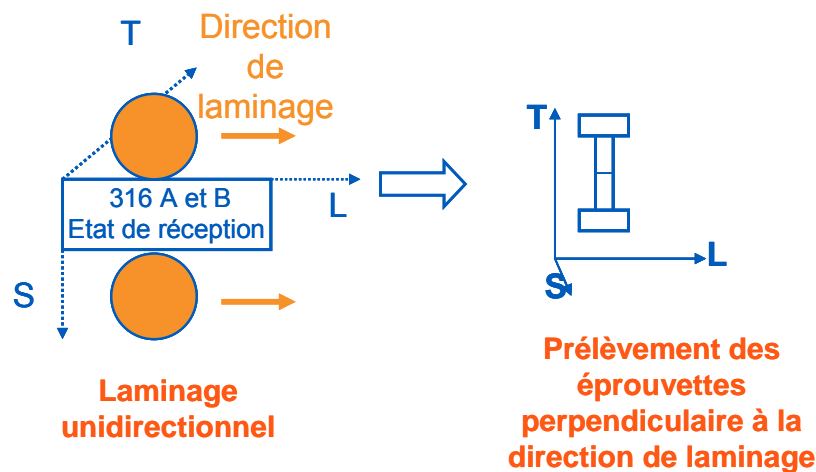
Laminage et prélèvement des éprouvettes en acier 316L A et B
